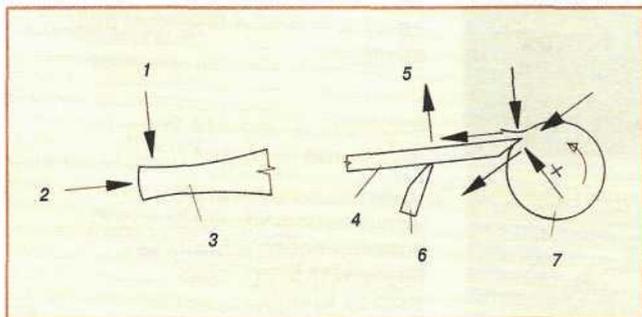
Силы, действующие на инструмент: 1 - отжимающая сила; 2 - осевая сила; 3 - ручка инструмента; 4 - лезвие инструмента; 5 - реакция подручника; 6 - подручник; 7 - деталь.
